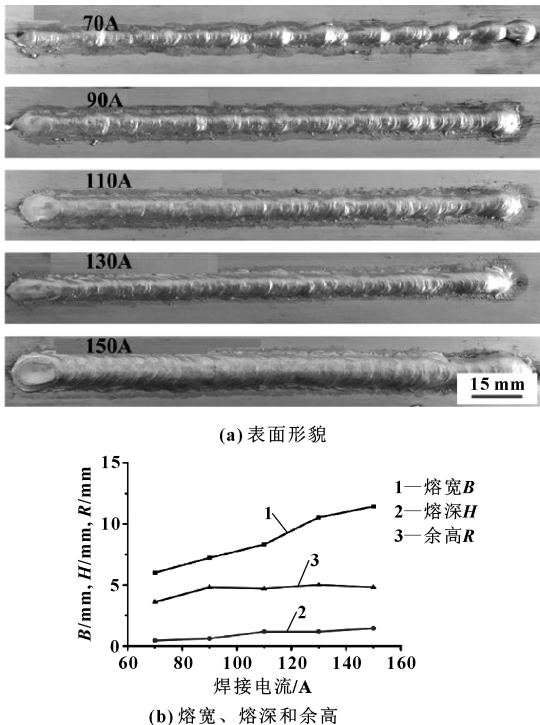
不同焊接电流下 6061 铝合金焊缝的表面形貌以及熔宽、熔深和余高
